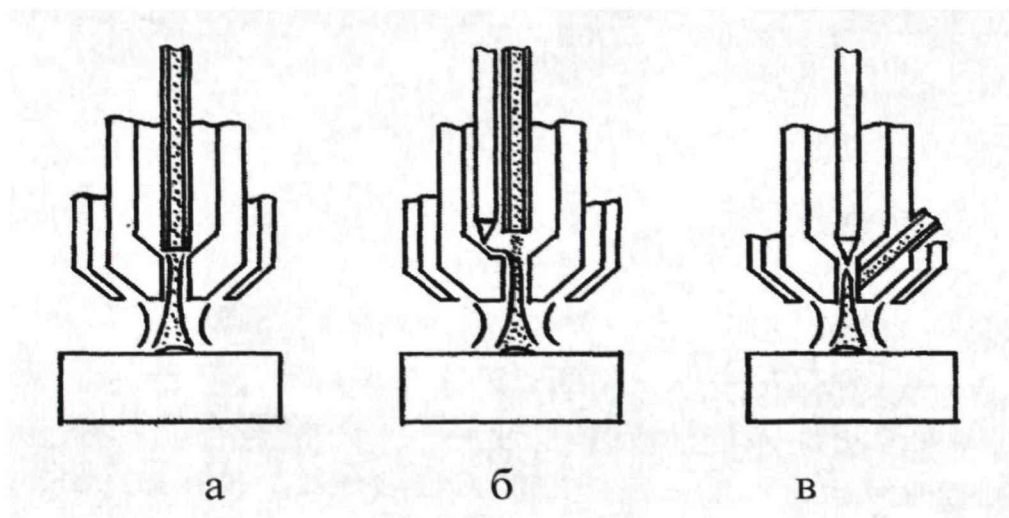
Схеми плазмового напавлення з подачею наплавочного матеріалу в стислу частину дуги
